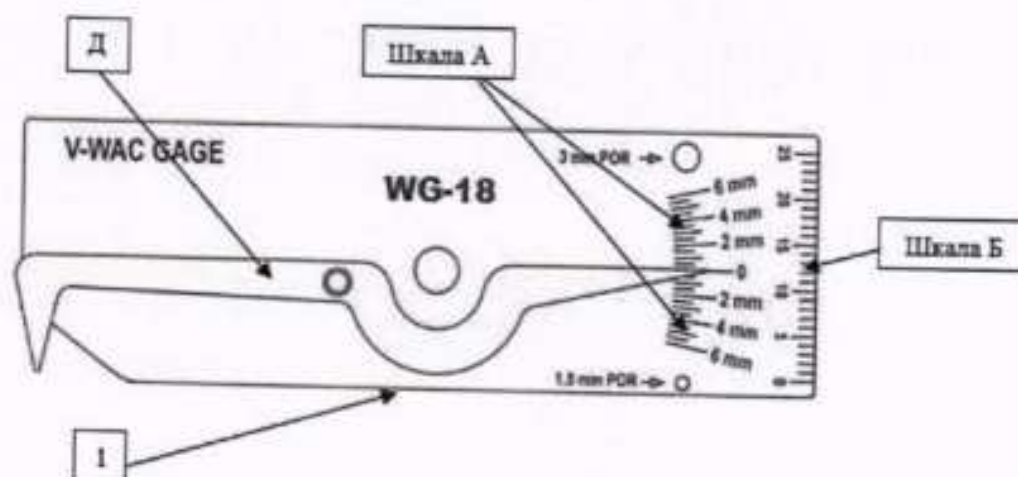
Общий вид шаблонов сварщика модели WG-18;
